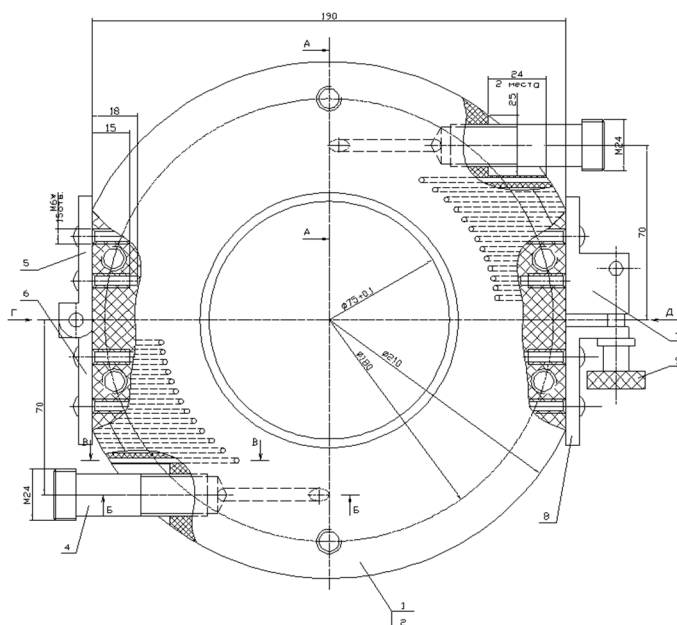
Конструкция специальной пневмодинамической камеры для упрочнения шеек коленчатых валов: 1- крышка; 2 - крышка; 3 - сегмент; 4 - резьбовой клапан; 5,6 - элемент петли; 7 - хомут; 8 - упор; 9 - головка резьбовая; 10, 11 – ось.
